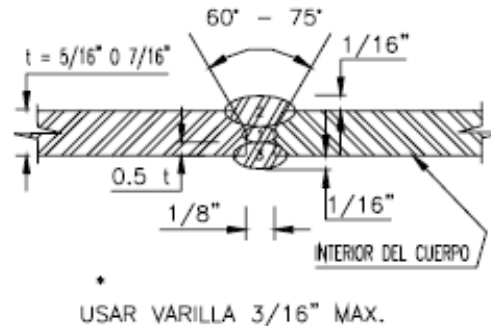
Tipos de soldadura a utilizar en el recipiente
